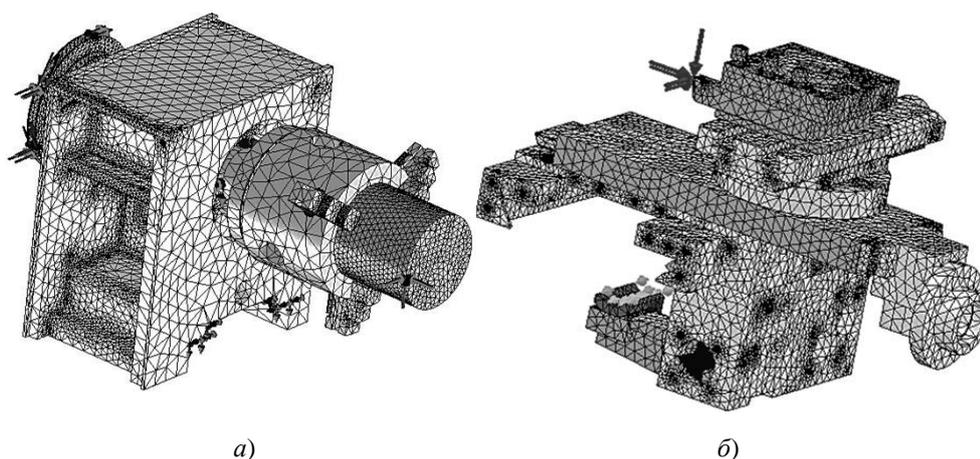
Трехмерные модели шпиндельной бабки (а) и суппорта (б) малогабаритного токарного станка
